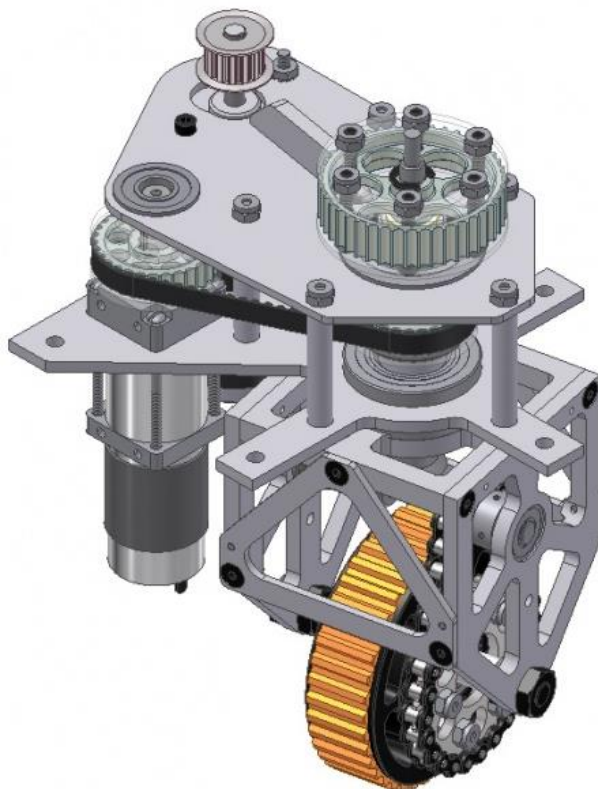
3D-модель поворотного вузлу FRC Team 1640
